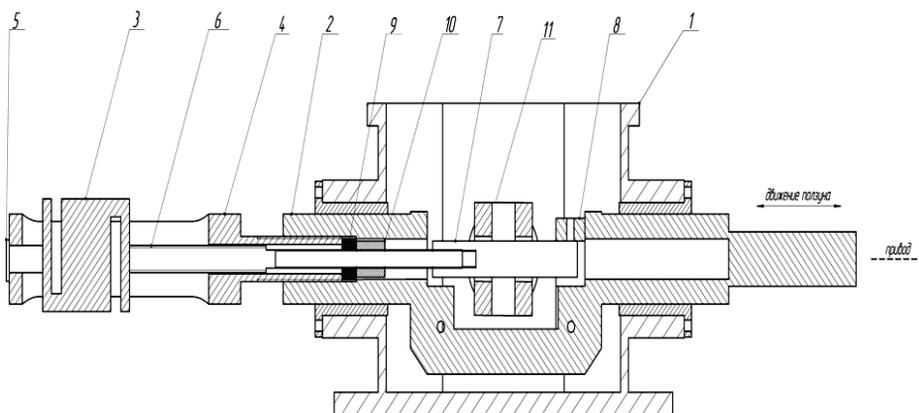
Схема испытательного узла модифицированной машины трения УМТ 2168М: 1- камера; 2 - ползун; 3 - тензодатчик; 4 - держатель; 5 - крепежный болт; 6-соединительный вал; 7 - держатель образца; 8 - направляющий блок; 9 - резиновое уплотнение; 10 - втулка; 11 - прижимной узел
